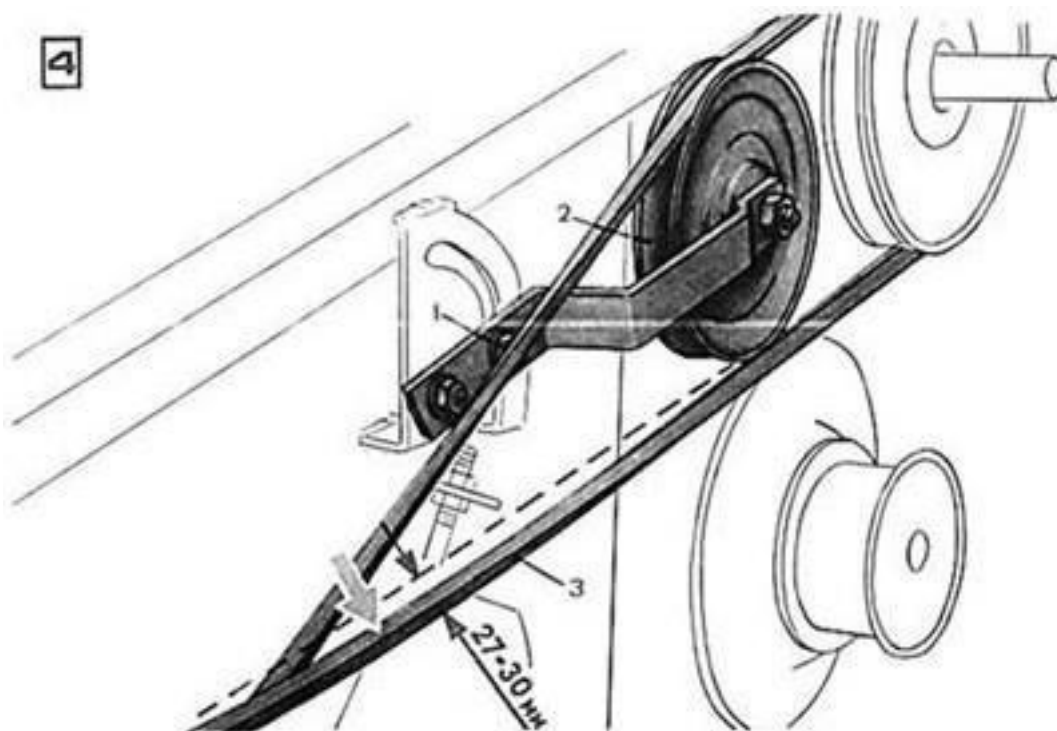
Схема регулировки натяжения приводного ремня:
